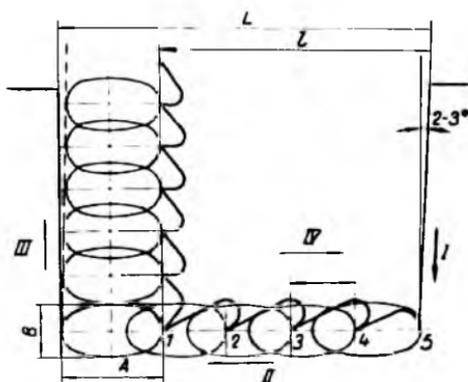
Схема движений зубьев (1—5) гнездовой фрезы
